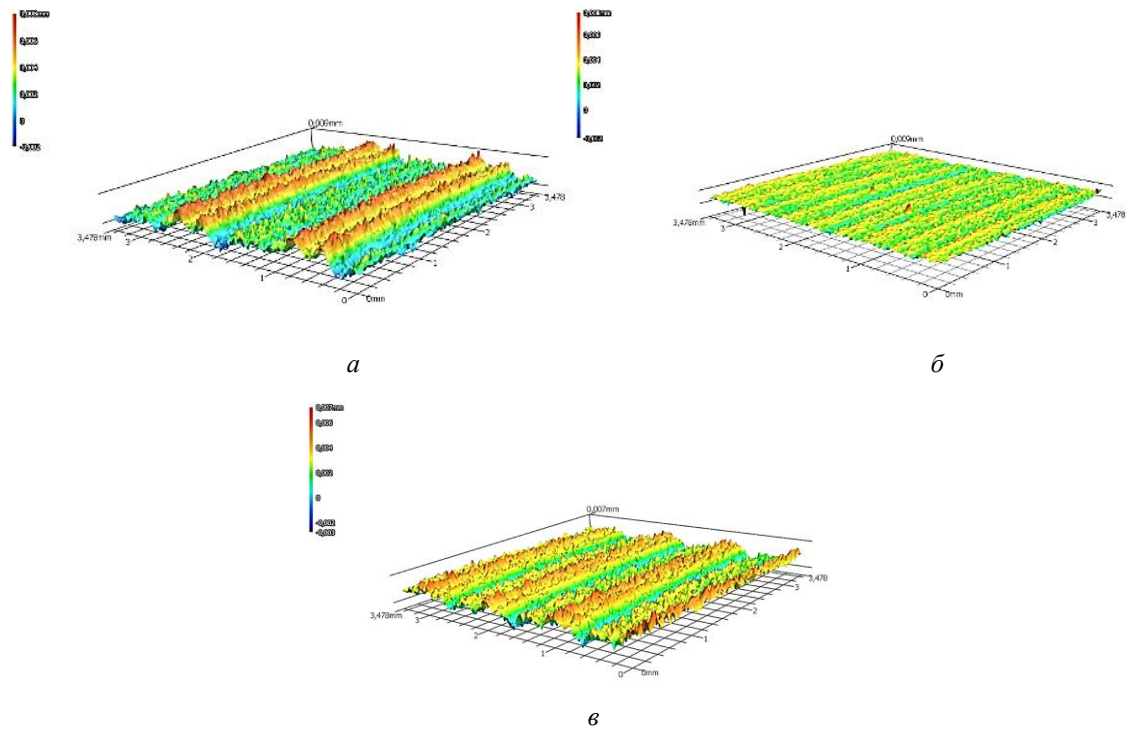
3D-графіки фрезерованих поверхонь (3x3 мм):
